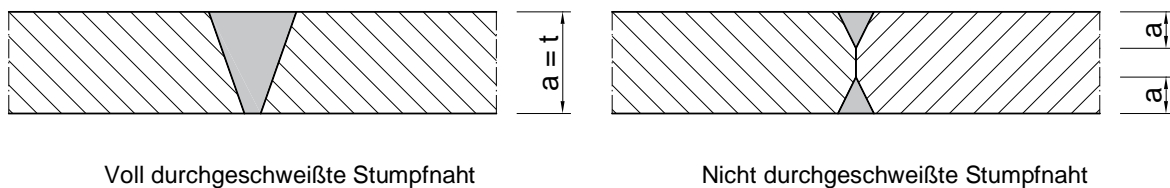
Unterscheidung einer durchgeschweißten und einer nicht durchgeschweißten Stumpfnah [58]
